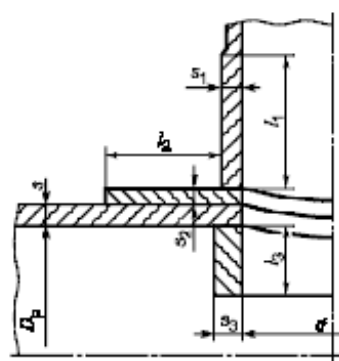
Основная расчетная схема соединения штуцера со стенкой сосуда[6, стр.19]
